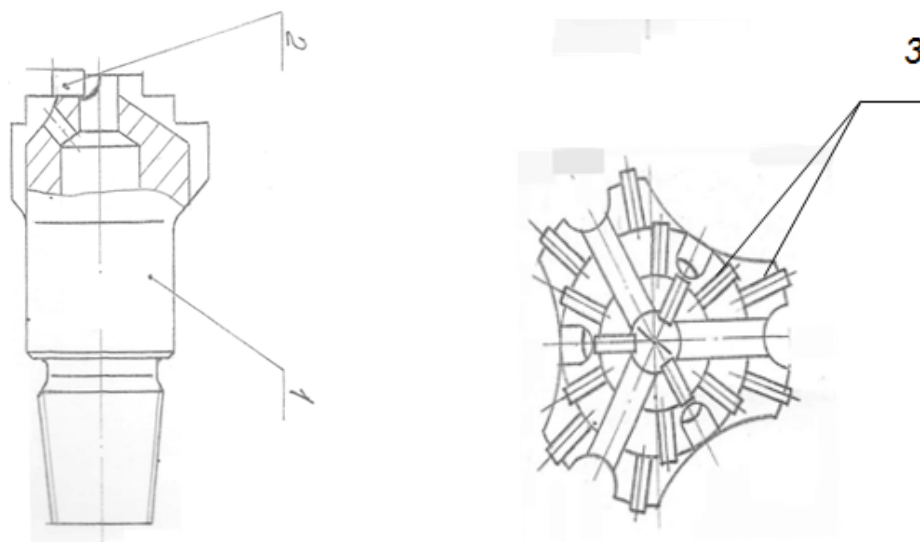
Ступенчатое долото режущего типа: 1- корпус, 2 – рабочий торец, 3- твёрдосплавные вставки
